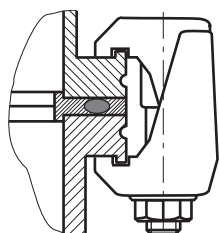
Flanschverbindung ISO-K zu ISO-K, Kammerschraube
